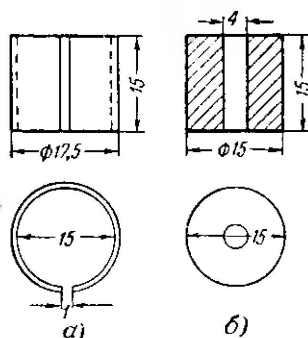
Приспособления для намотки звуковой катушки громкоговорителя.
